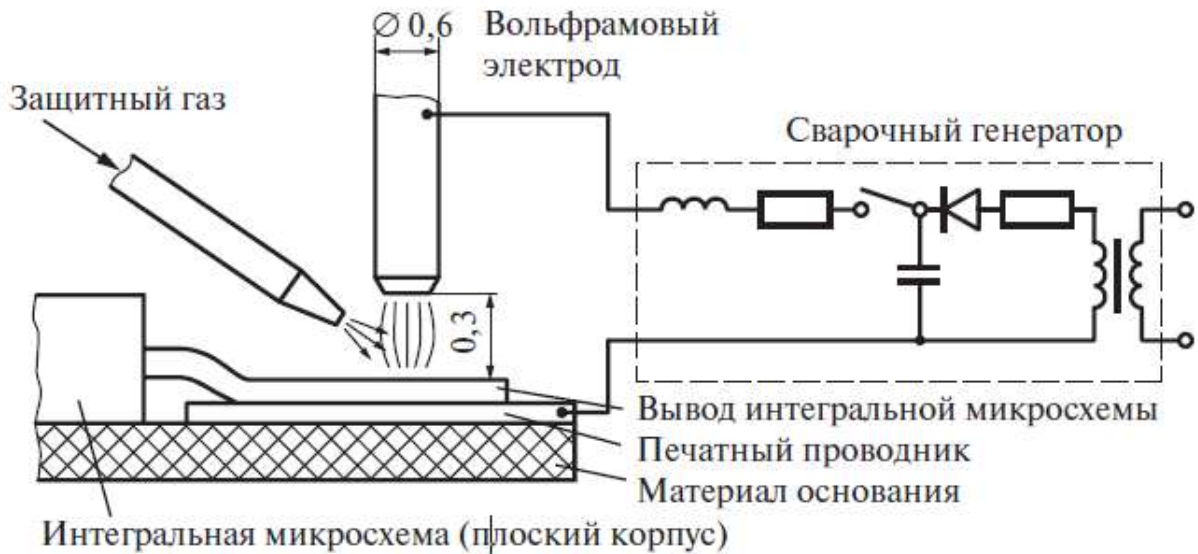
Принцип точечной электродуговой сварки
